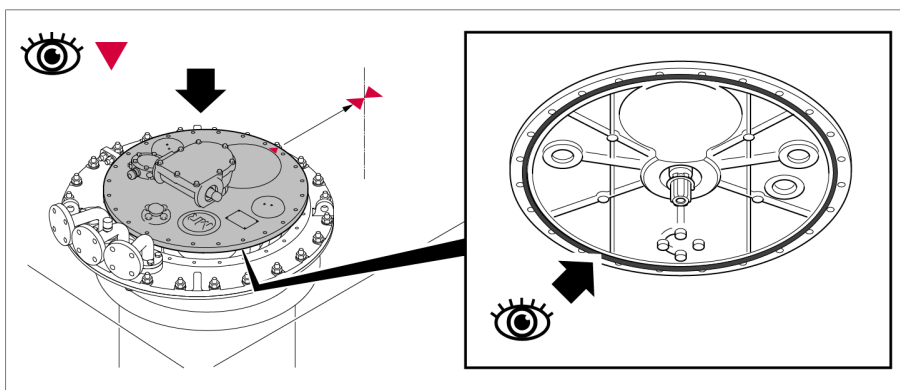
Laststufenschalterkopfdeckel mit O-Ring
